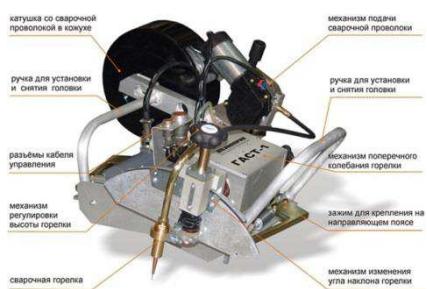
Универсальная сварочная головка ГАСТ-1
